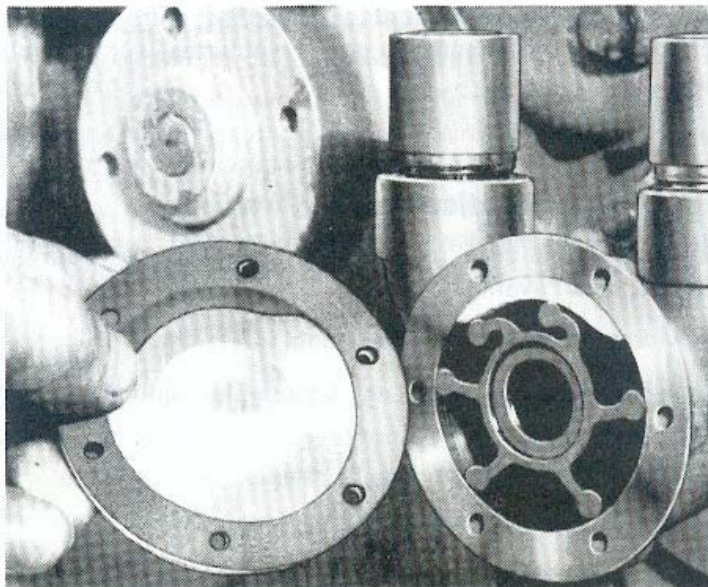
Dépose du couvercle de pompe à eau de mer.
